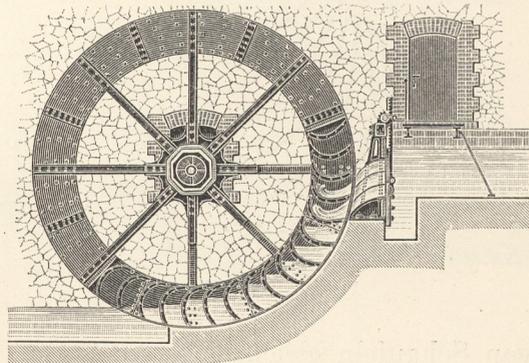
Mittelschlächtiges Wasserrad der Merseburger Maschinenfabrik Herrich & Co.
